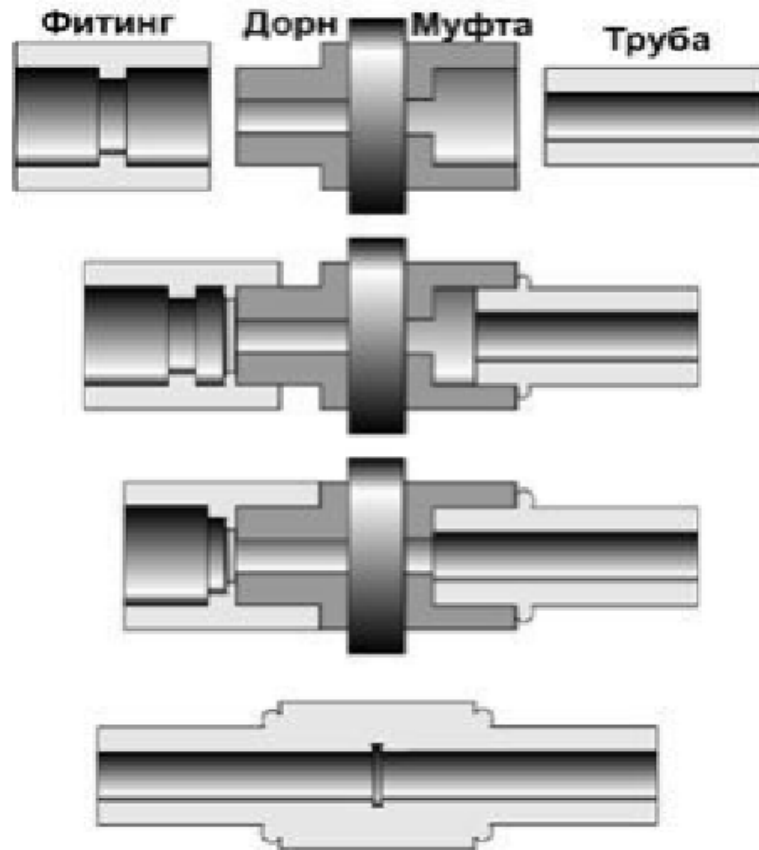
Схема зварювання нагрітим інструментом в раструб
